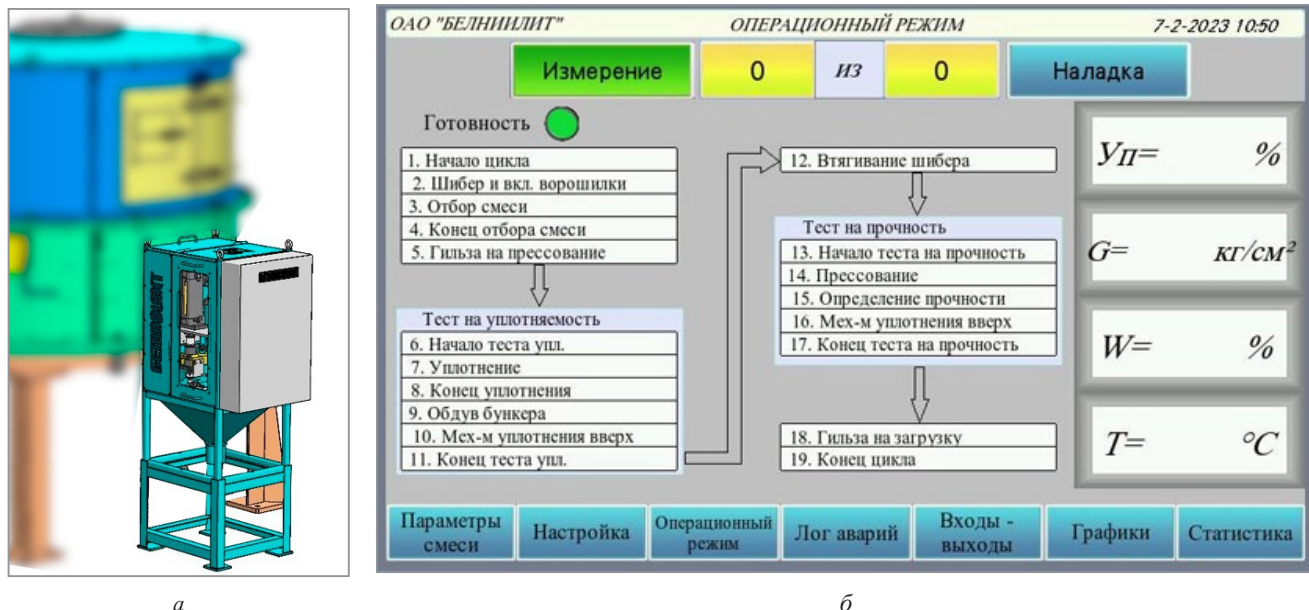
Общий вид автоматизированной системы контроля качества формовочной смеси модели П1937 конструкции ОАО «БЕЛНИИЛИТ», установленной на вихревой смеситель: а – панель оператора; б – мнемосхема
